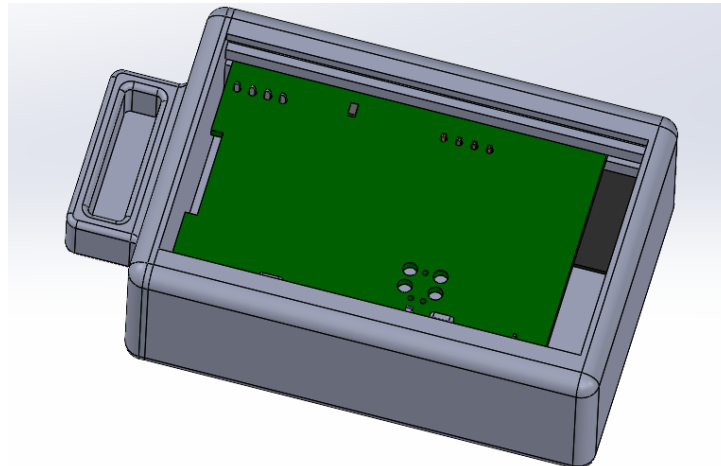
Vue 3D de l'assemblage du boîtier avec PCB
